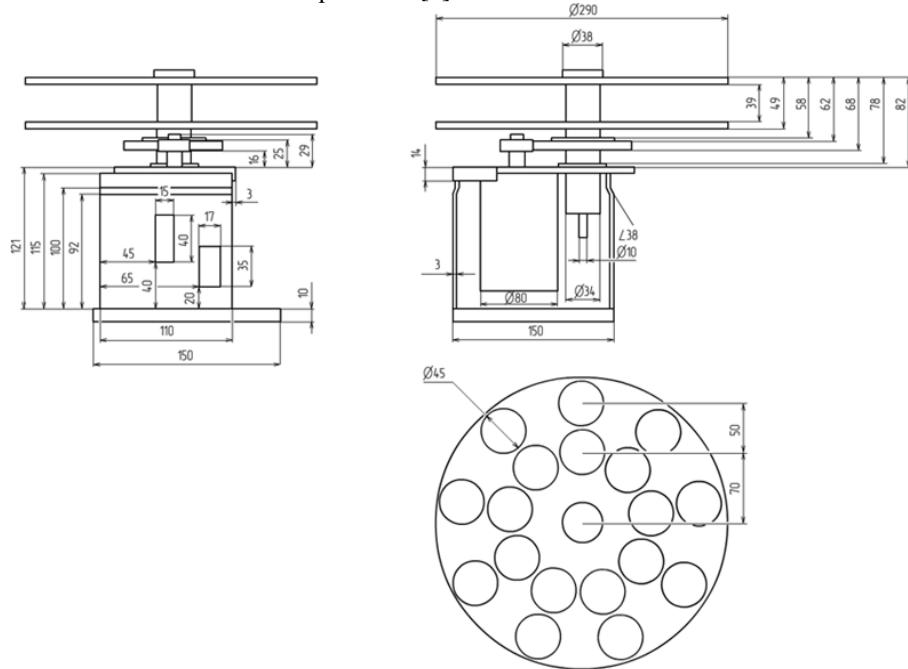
Шаговый двигатель 2ДШ78-0,16-1
